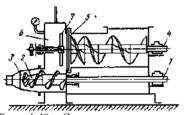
Схема ленточного вакуум-пресса: 1 – главный шнековый вал; 2 – прессующий шнек; 3 – цилиндр; 4 – вал смесителя; 5 – решётка; 6 – вакуум-камера; 7 – ножи
